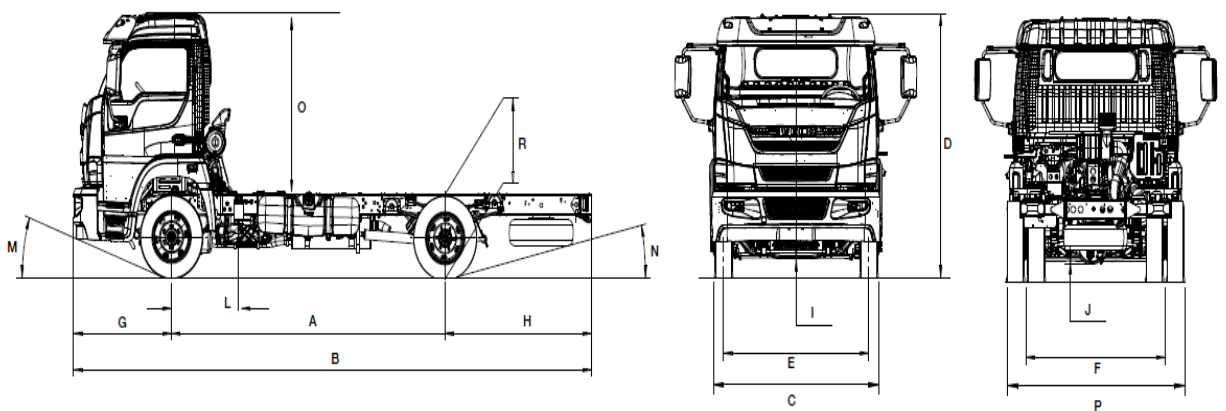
Dimensões Principais (mm) Iveco 90V16 e 130V18
